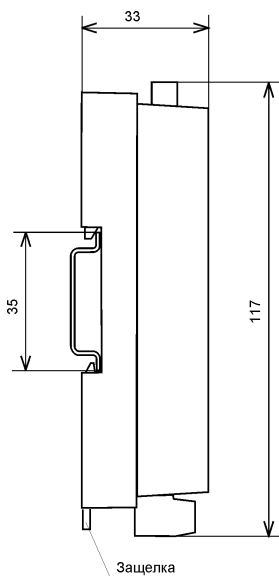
Габаритный чертеж модуля с креплением к DIN-рейке. Вид сбоку
